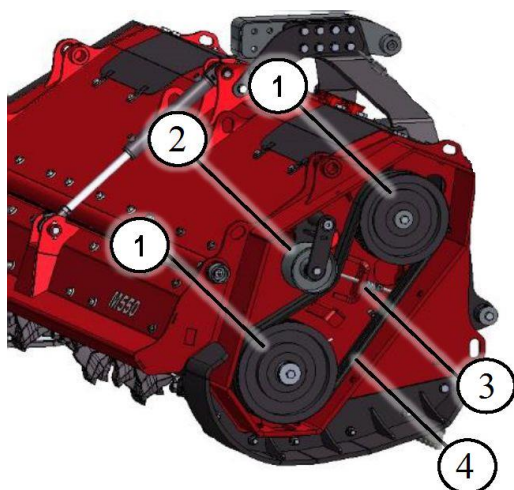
Ленточный привод мульчирующей фрезы, слева
